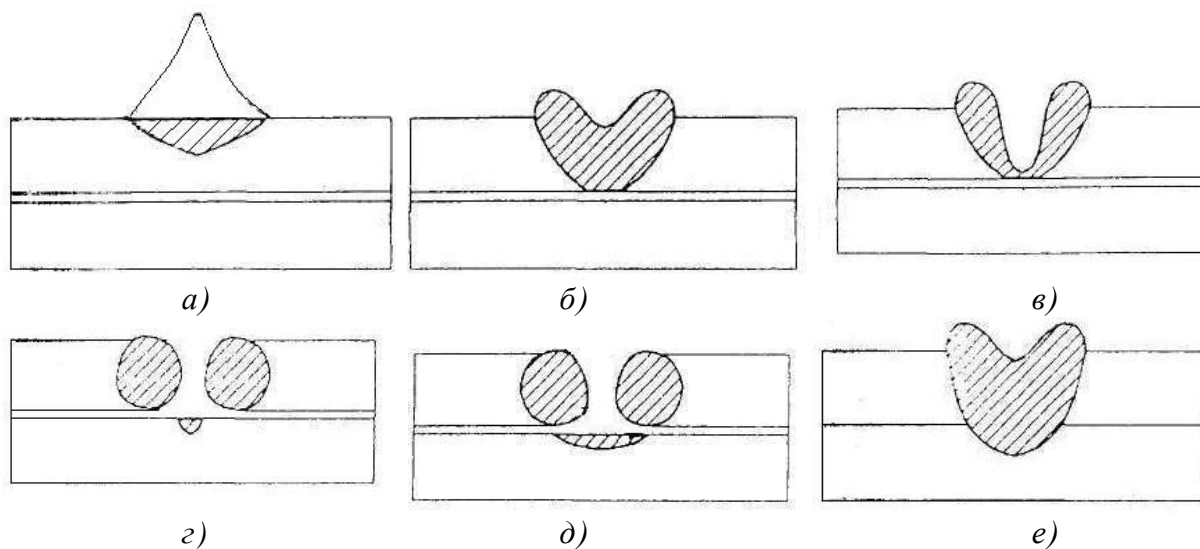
Этапы плавления деталей при плазменной точечной сварке
